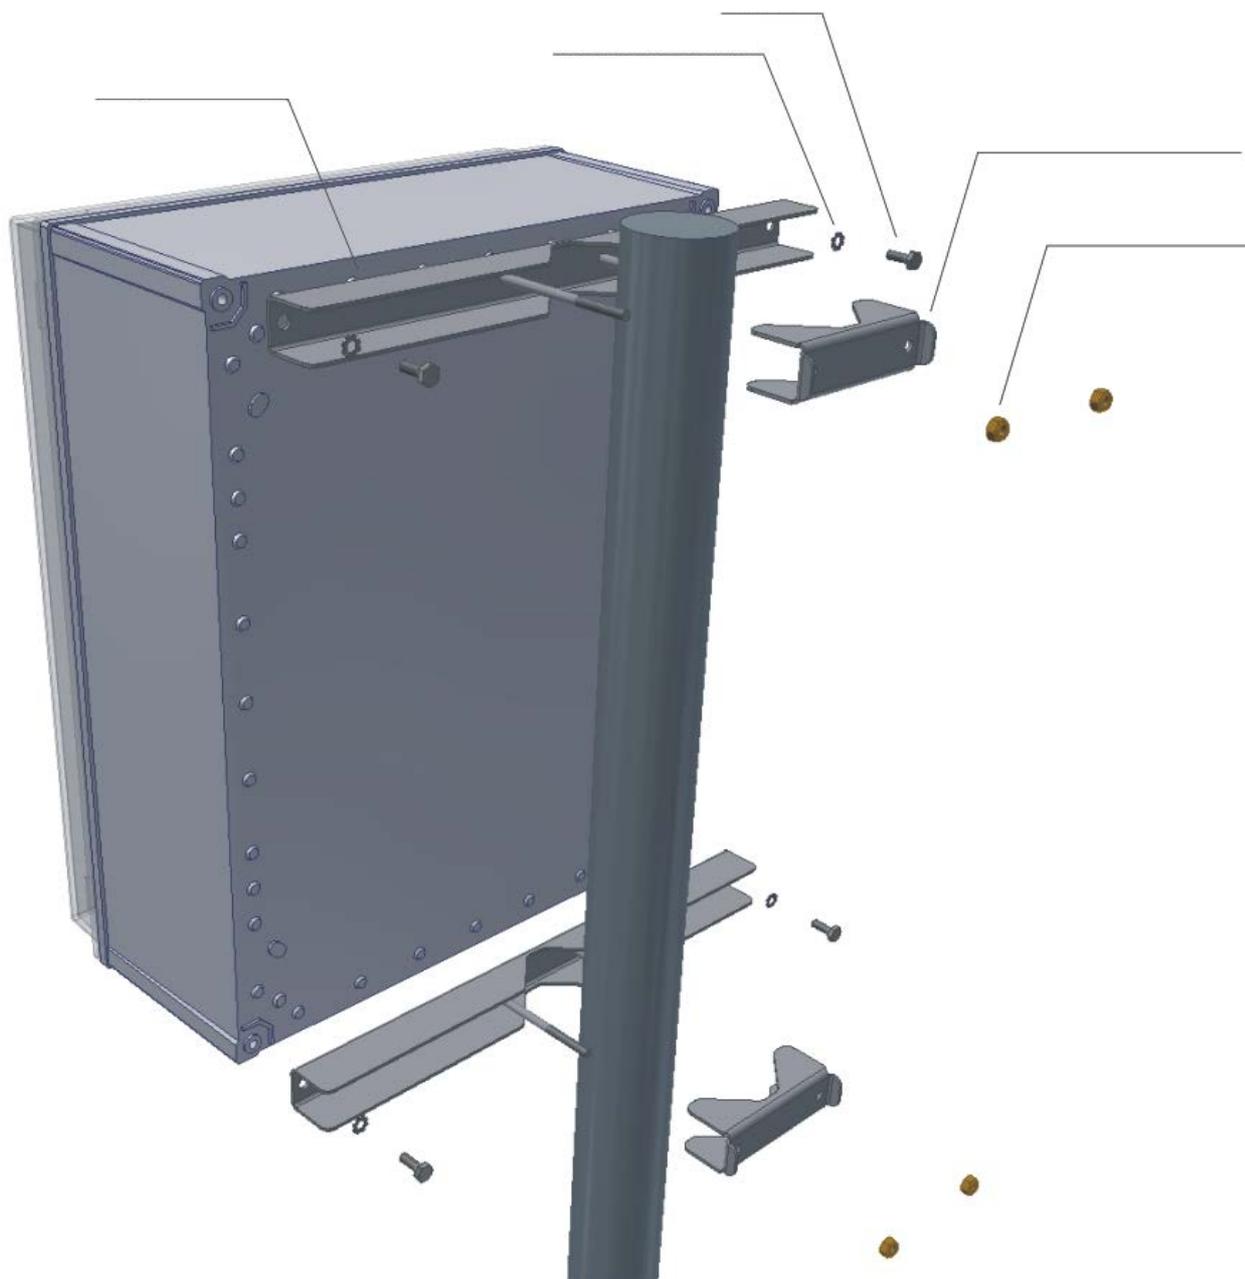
Крепление на столбе шкафа для наружного монтажа
